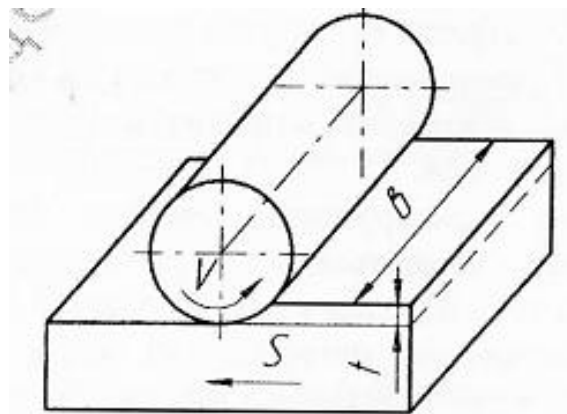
Елементи режимів різання при фрезеруванні циліндричною фрезою
